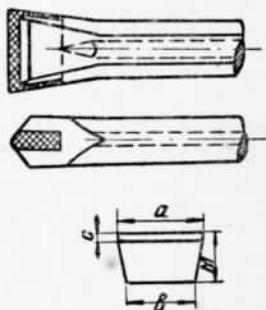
Однодолотчатый бур, армированный пластинкой из твердого сплава «победит РЭ-8»; внизу пластинка из твердого сплава
